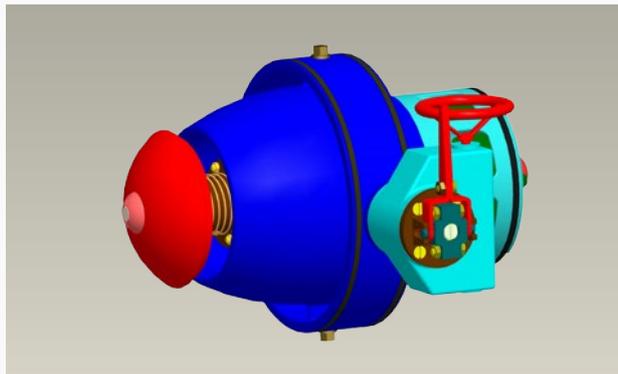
Универсальный невозвратно-управляемый клапан с осевым течением потока рабочей среды с демонтированными полукорпусами
